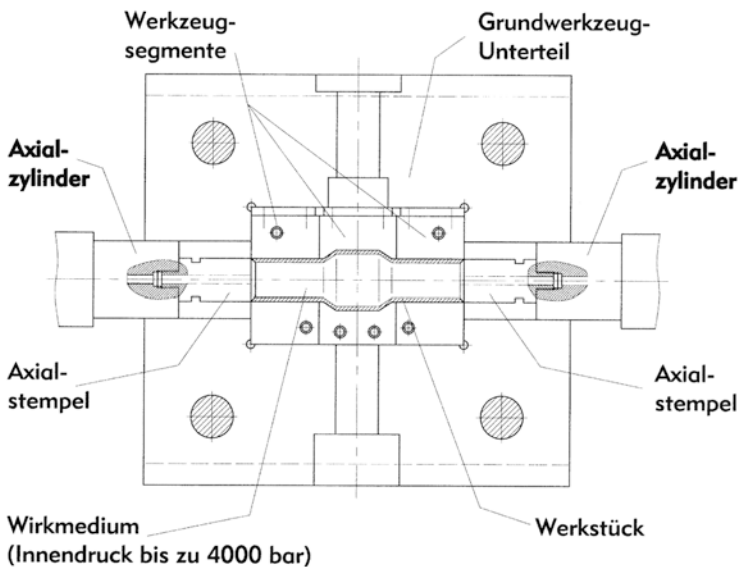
Innendruckumformen mit segmentiertem Werkzeug, separatem Druckübersetzer verbunden mit Werkzeugschließkopf über elastisches Hochdruckelement nach Fraunhofer Institut IWU [81]
